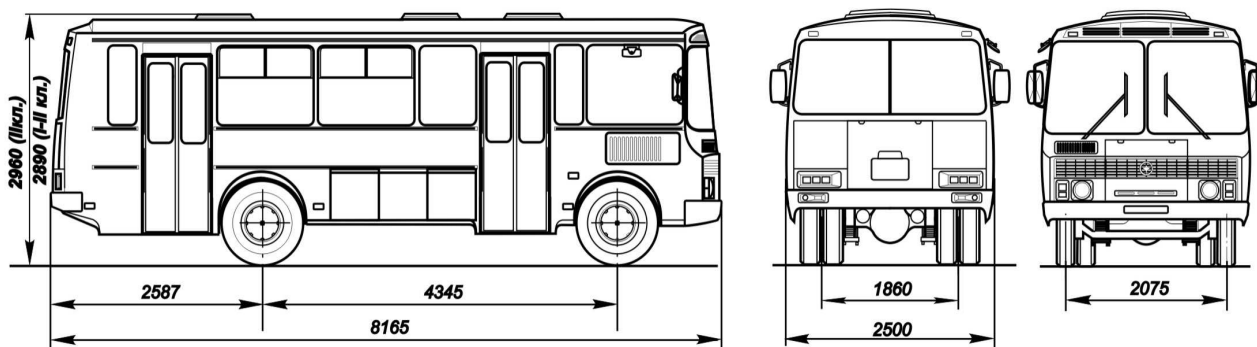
Габаритные размеры автобуса ПАЗ-4234-04
